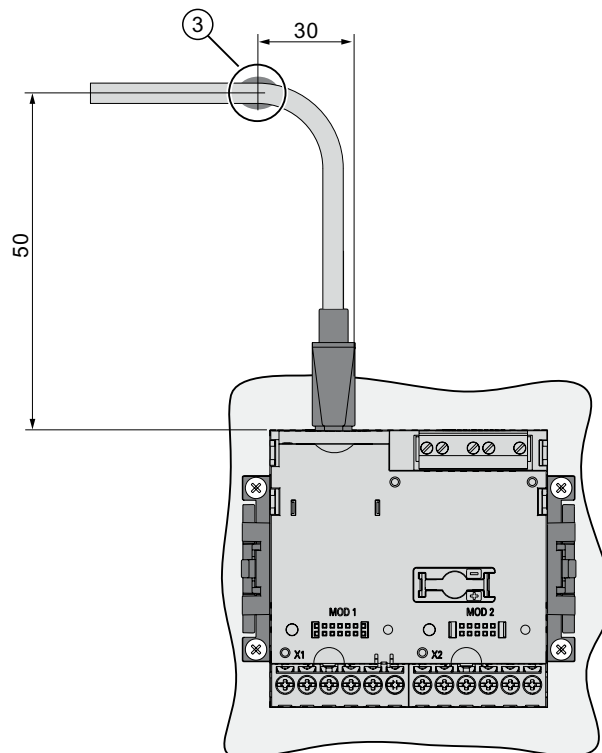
Montageschritt E - Zugentlastung für RJ45-Stecker
